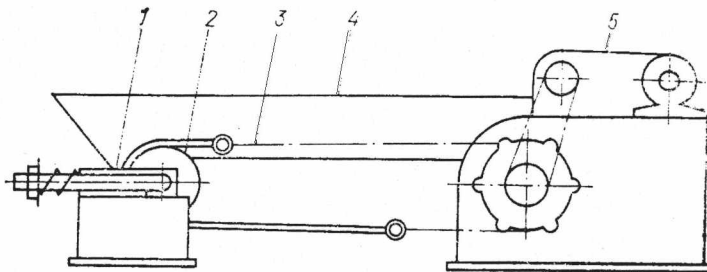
Конструктивно-технологічна схема роздавача РВК-Ф-74: 1 - натяжна станція; 2 - ведений барабан; 3 - робочий орган; 4 - годівниця; 5 - приводна станція.
